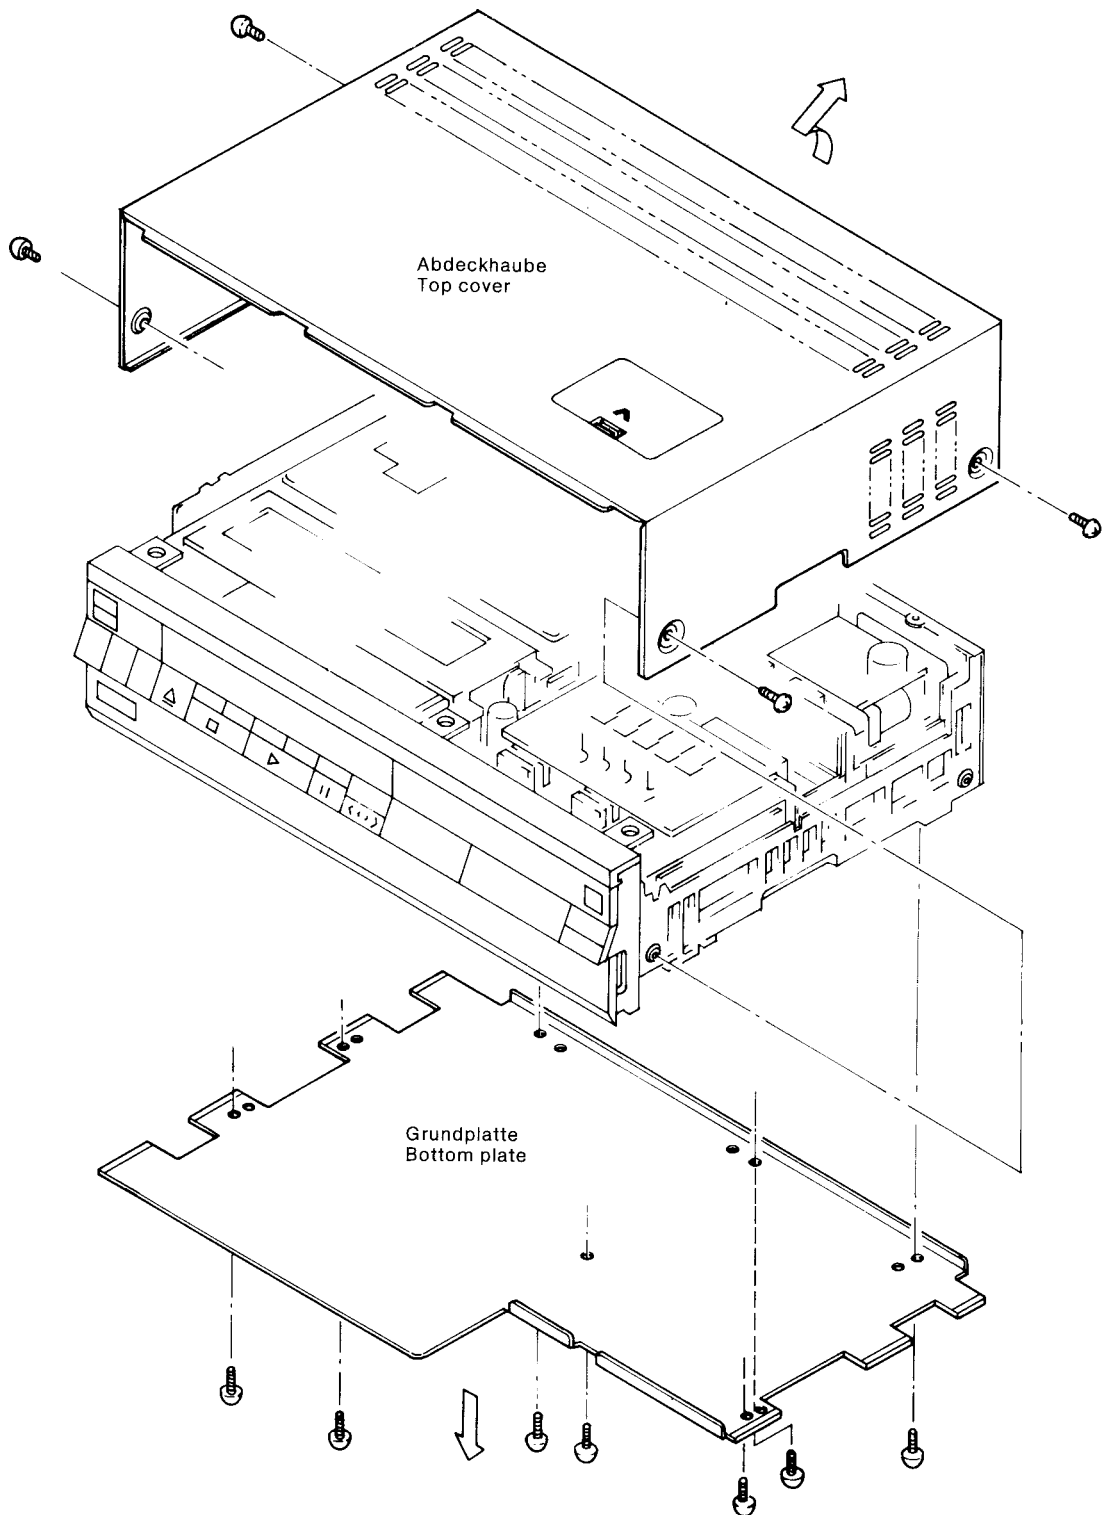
Gehäuseabdeckungen /
